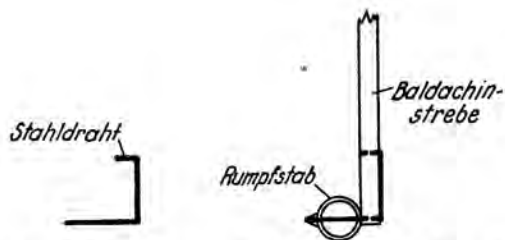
Befestigung einer Baldachinstrebe am Rumpfstab
